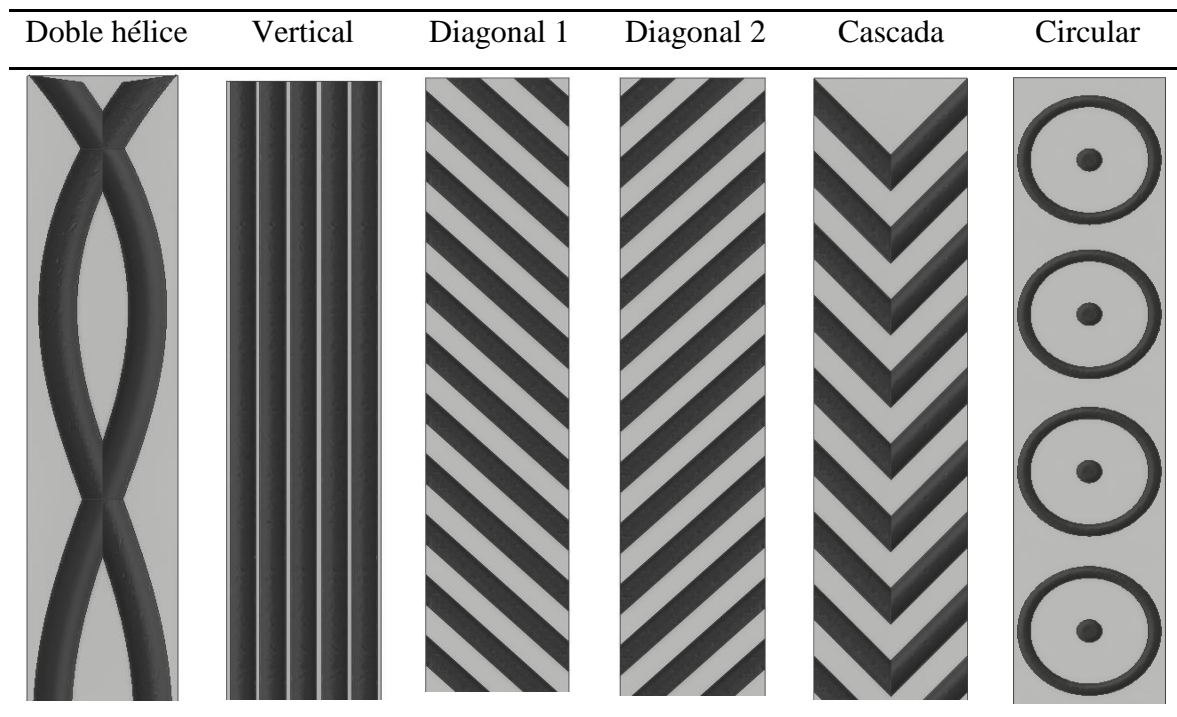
Modelos geométricos para la soldadura de blindaje.
